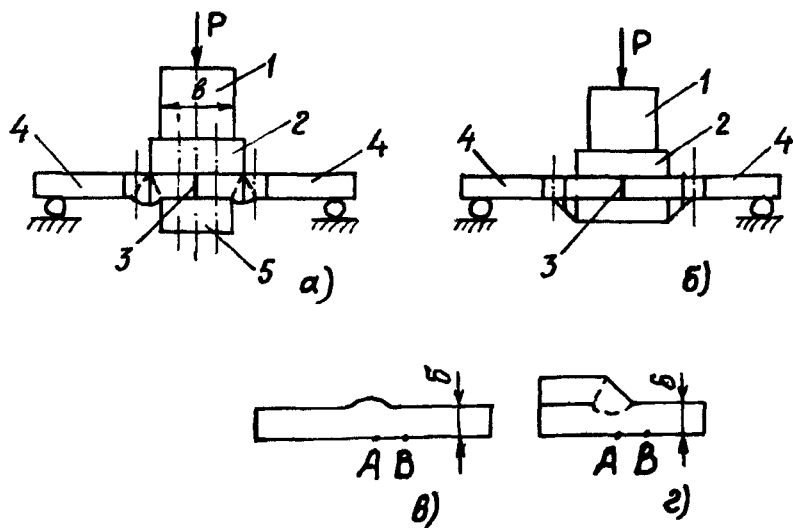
Сваренные образцы для испытаний на изгиб:
